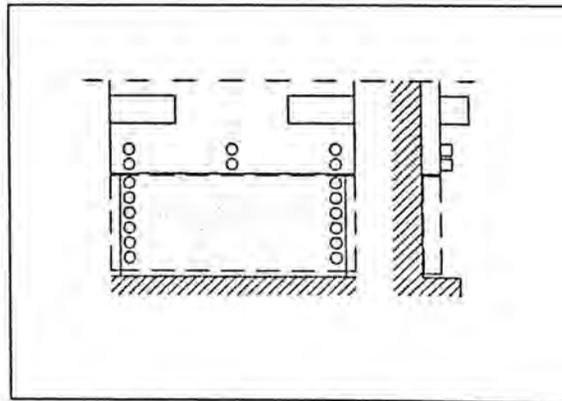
Vorhandener Bauraum für die zu konstruierende Grundplatte
